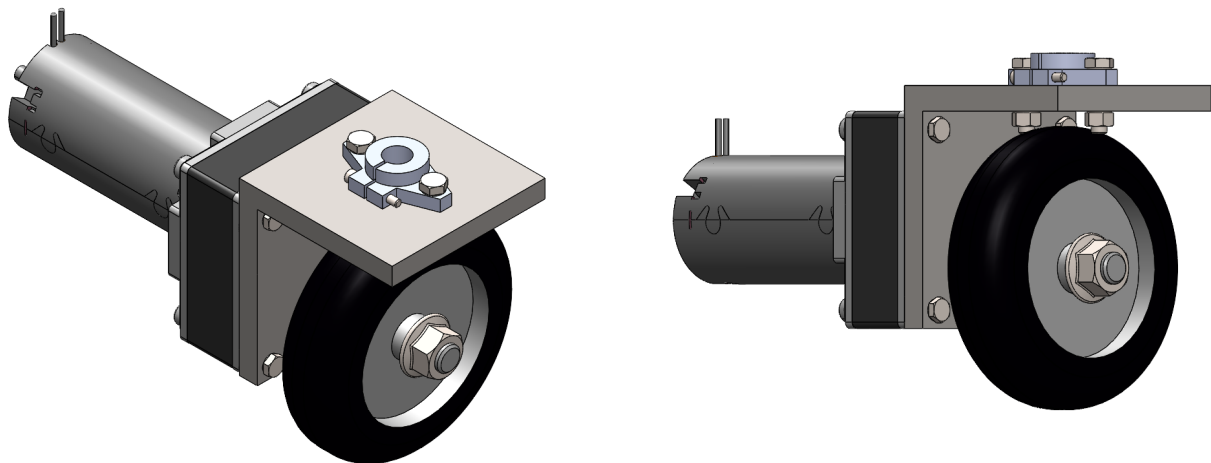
Sous-ensemble groupe de propulsion avant de la plateforme mobile (vue isométrique et vue de coin)
